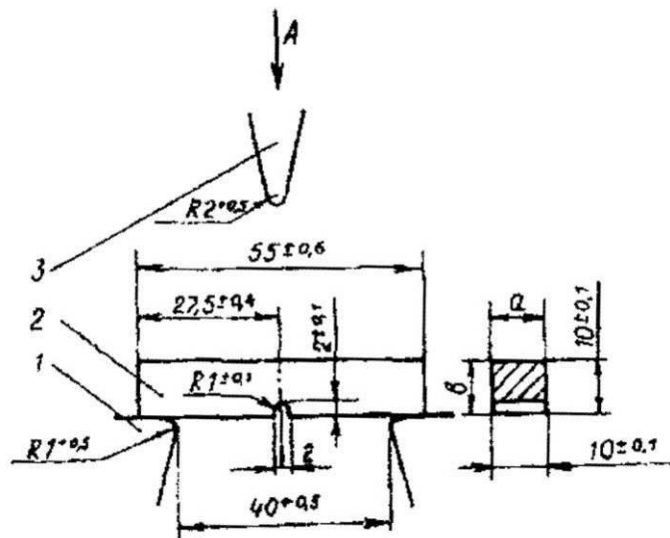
Конструкція зразка з U-подібним надрізом та схема випробовування на ударну в'язкість: 1 - опора зразка; 2 - зразок; 3 - ніж маятника копра; А - напрям удару
